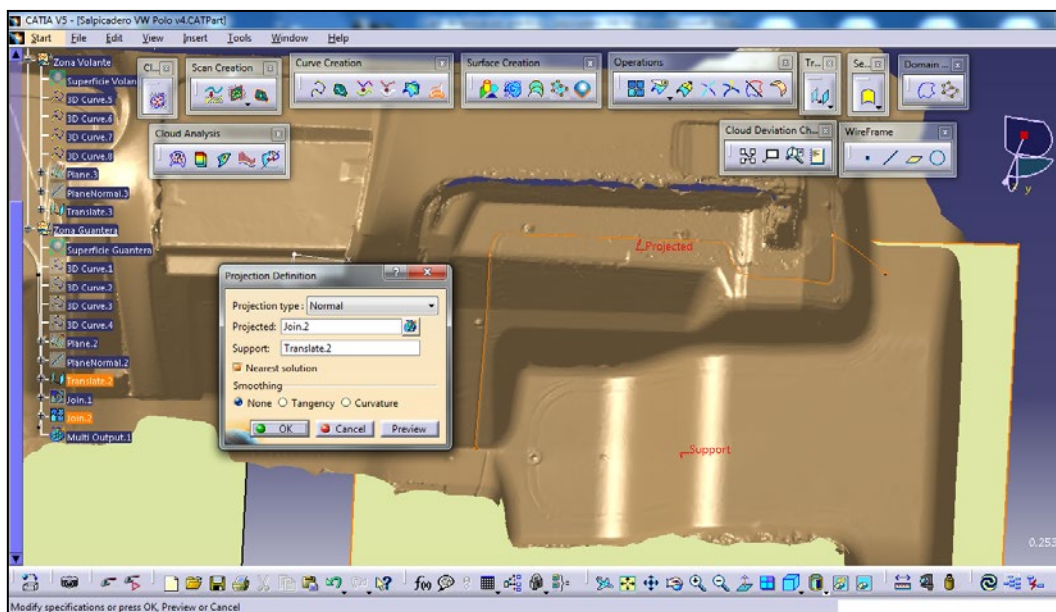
Creación del plano desplazado del plano de apoyo de la zona de la guantera.
